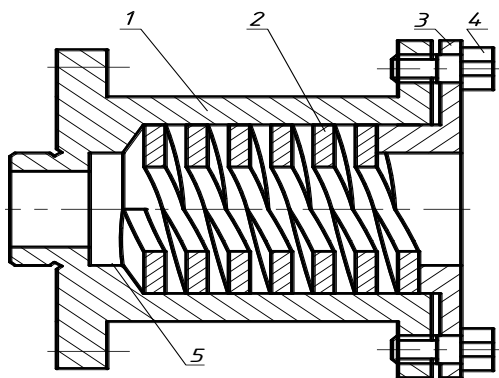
Конструкція пристрою для розточування нежорстких гвинтових деталей
